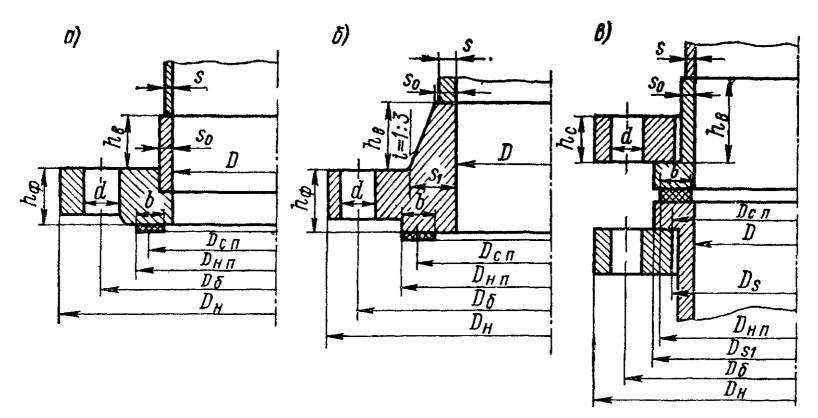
Типы фланцев: a — плоский приварной; δ — приварной встык; в — свободный
